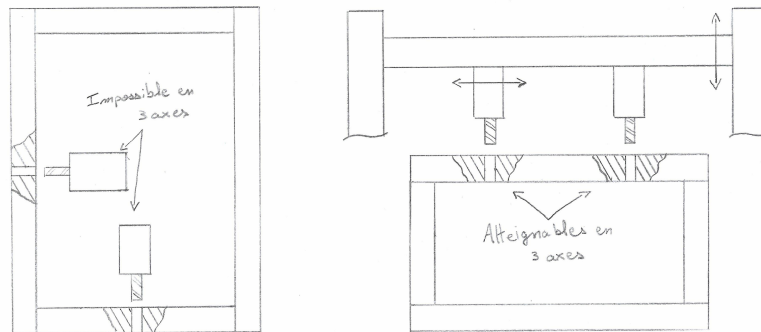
Étude de faisabilité : usinage de la structure après soudure
